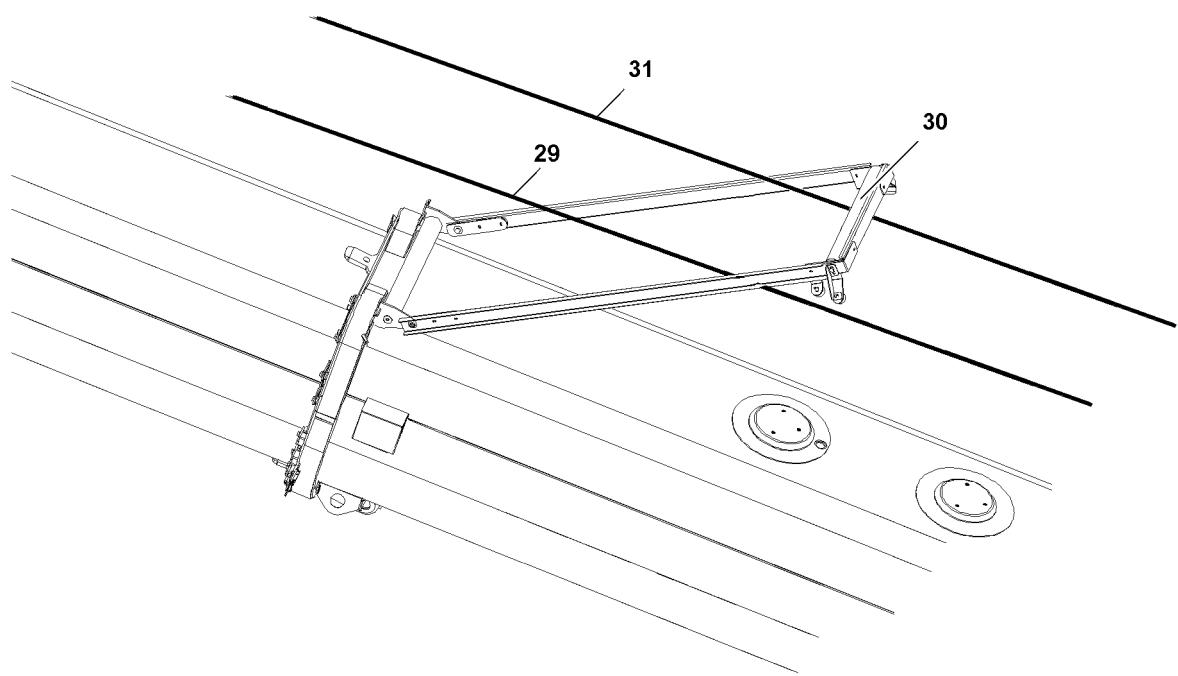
Recorrido del cable de elevación debajo del estribo del cable de elevación 30
